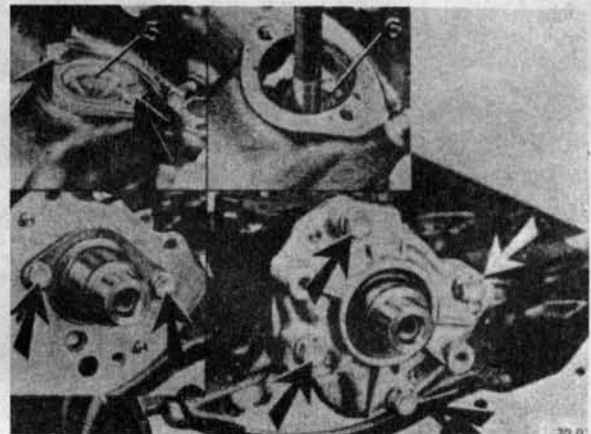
Снятие промежуточного вала двигателя В172
